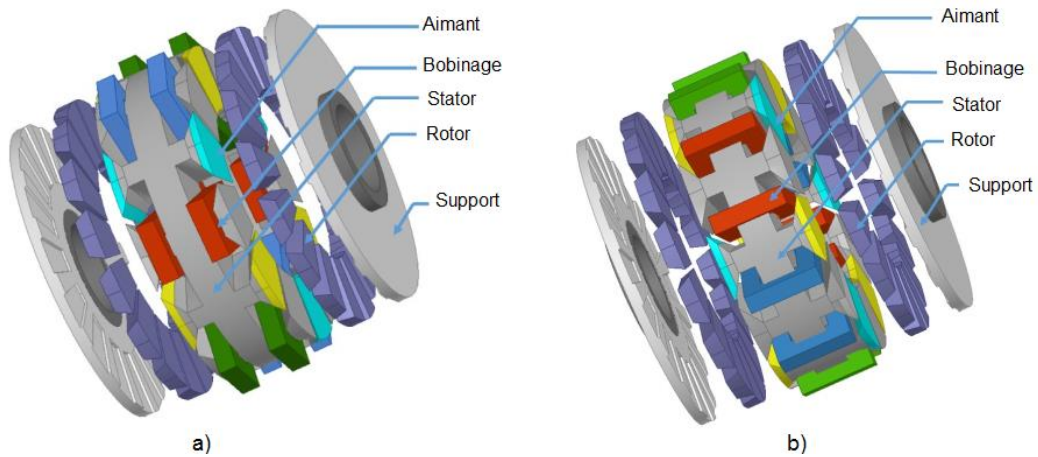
Machines à flux axial stator double rotor à commutation de flux a) structure a bobinage sur dents b) structure a bobinage toroïdal [24]
